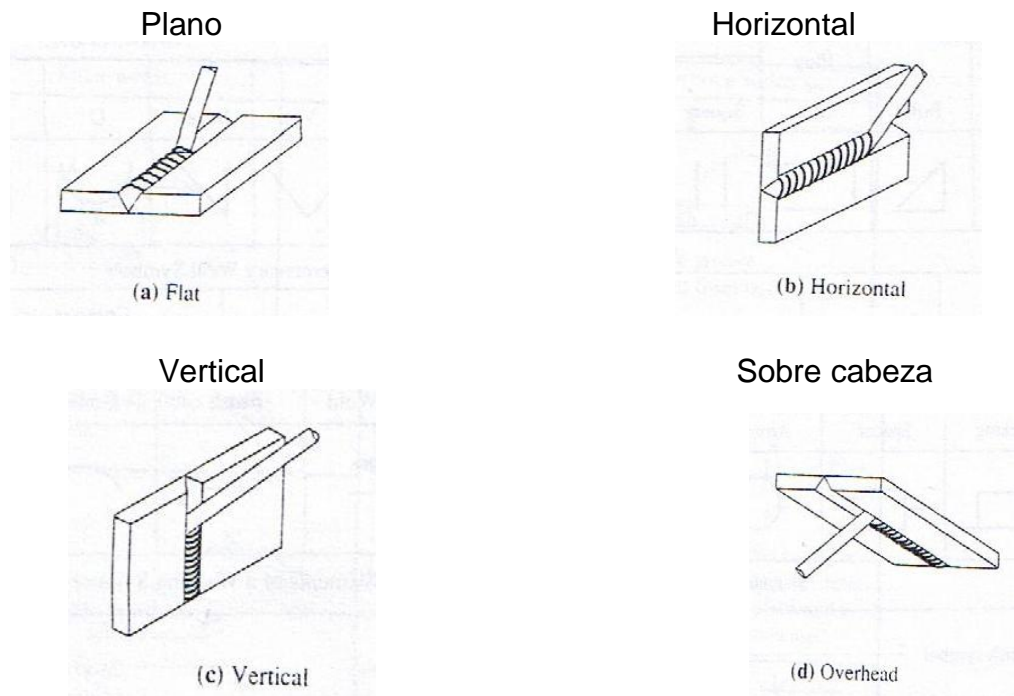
Posiciones de soldadura del S.A.P.<sup>6</sup>
